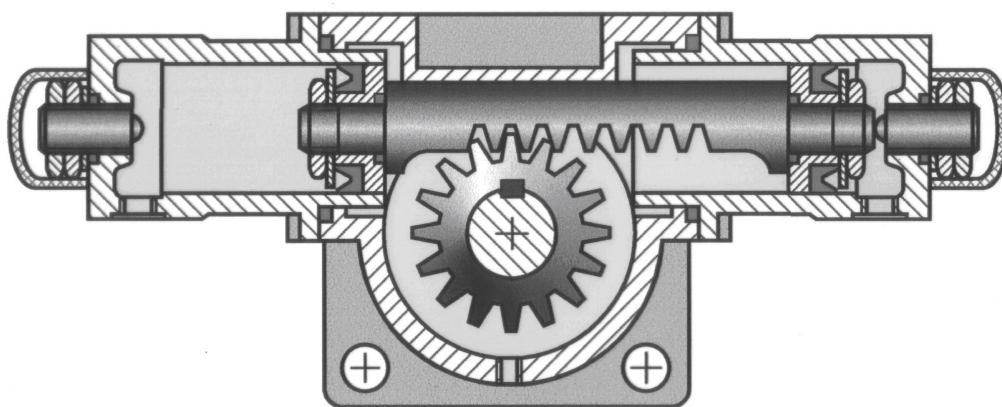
Гидродвигатель поворотного действия поршневого типа
